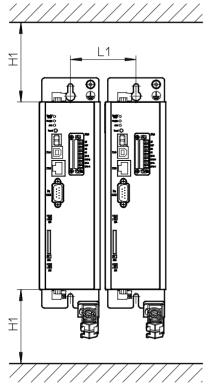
Motorcontroller CMMP-AS-...-M0: Montageabstand und Einbaufreiraum
